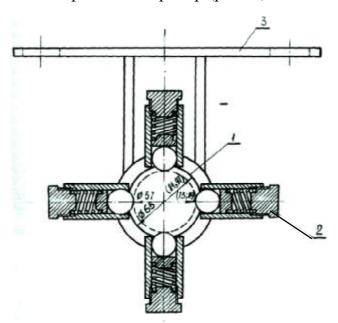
Шаровой центратор в разрезе: 1 – кольцо; 2 – опора центратора; 3 – центратор
